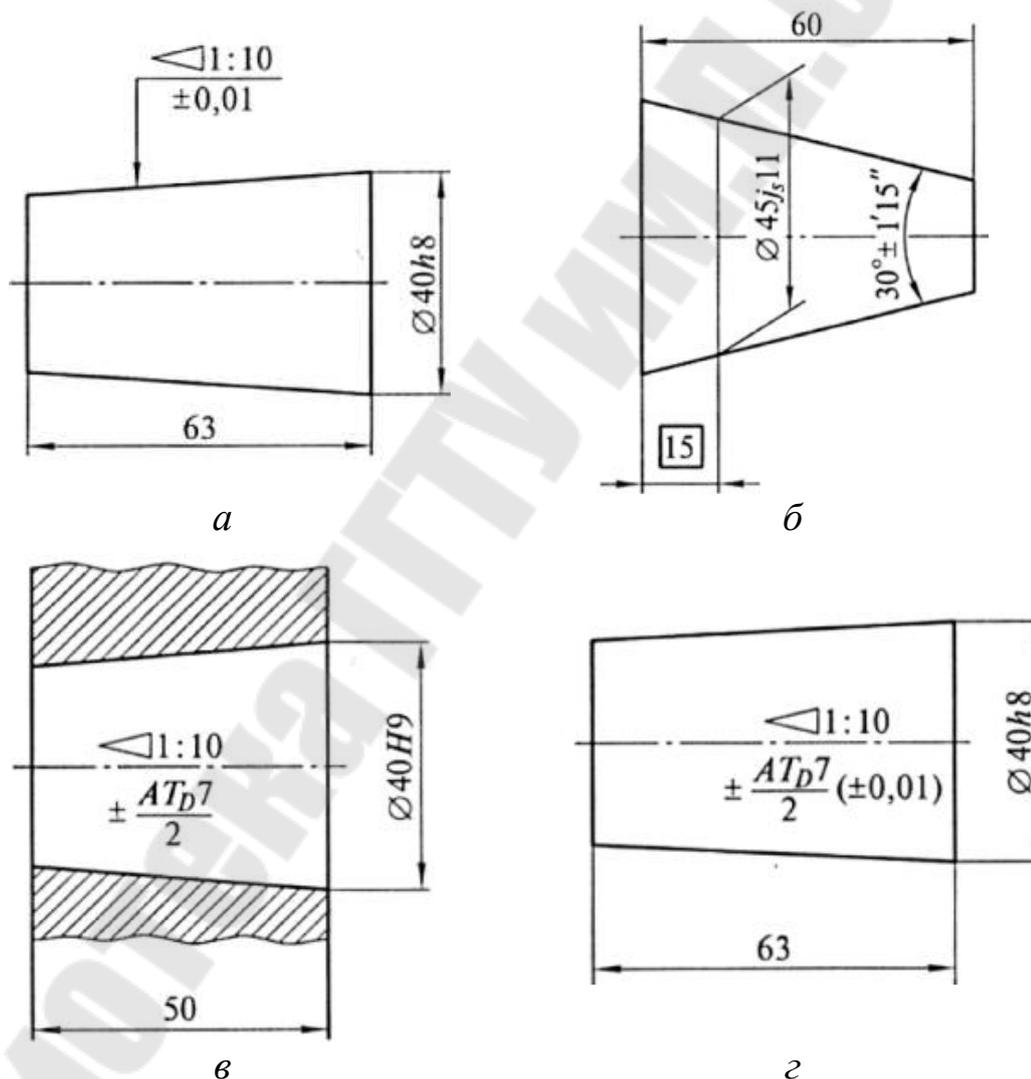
Числовой (*а, б*), условный (*в*) и смешанный (*з*) способы обозначения допусков конусов на чертежах
